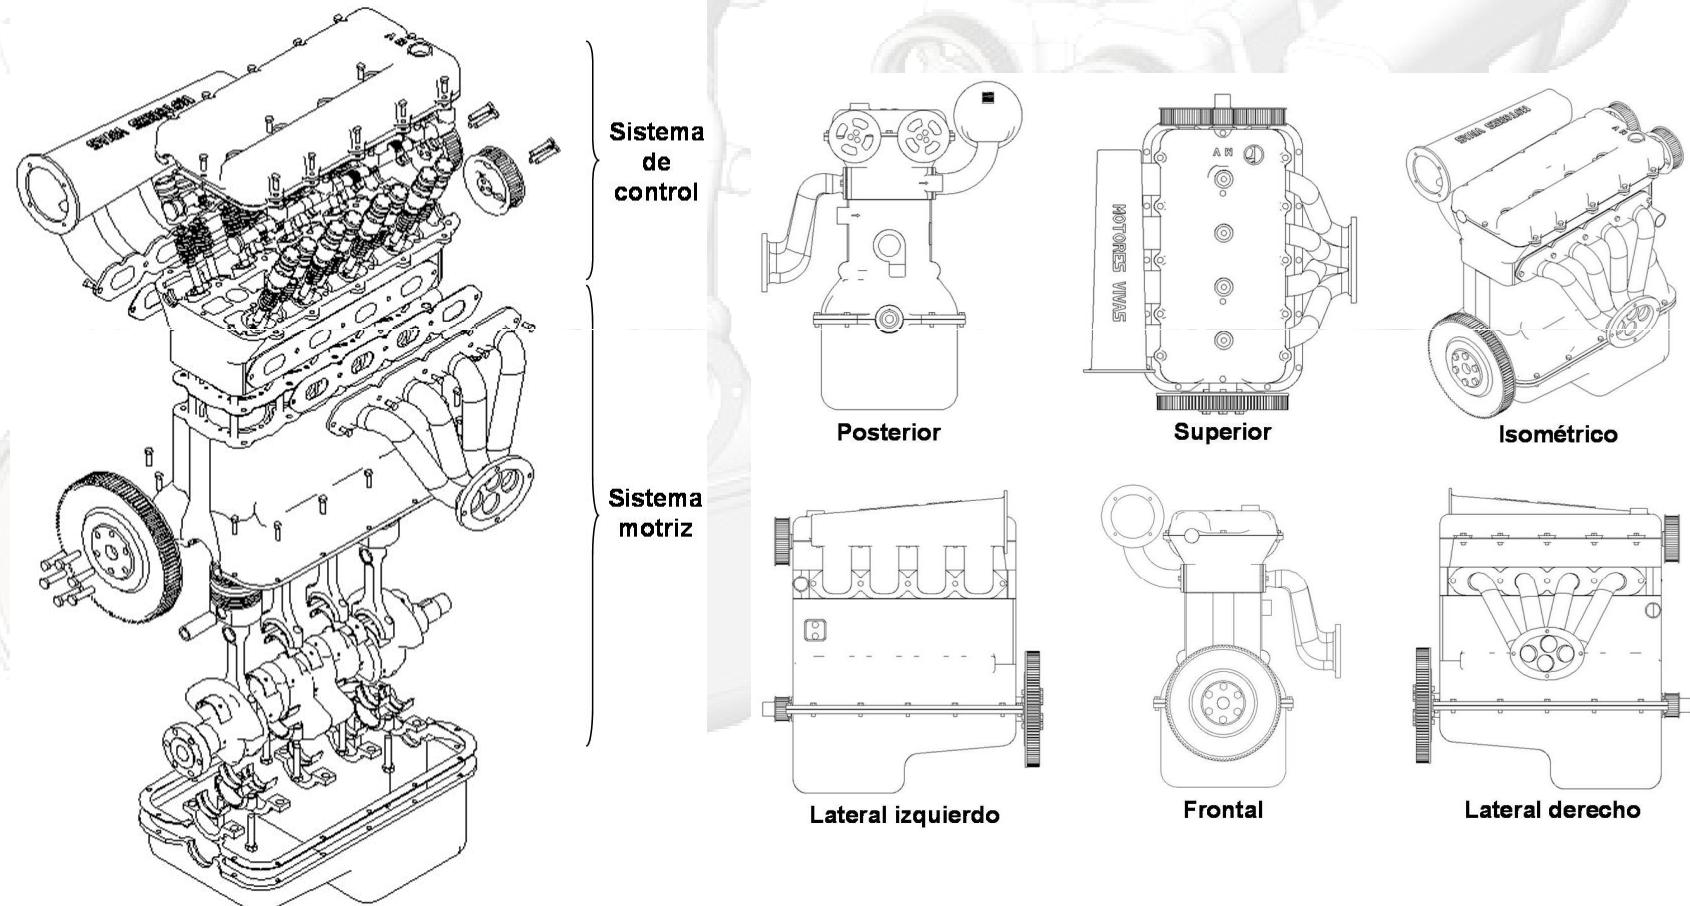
PLANO DE DESPIECE Y DE MOTOR ENSAMBLADO
